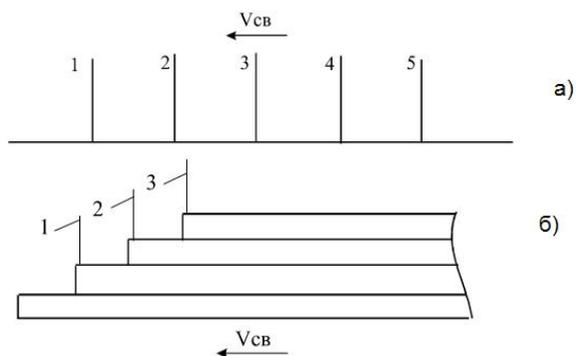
Схемы выполнения процесса автоматической сварки под флюсом: *а* – методом многоголовочной сварки; *б* – методом «тандем»
